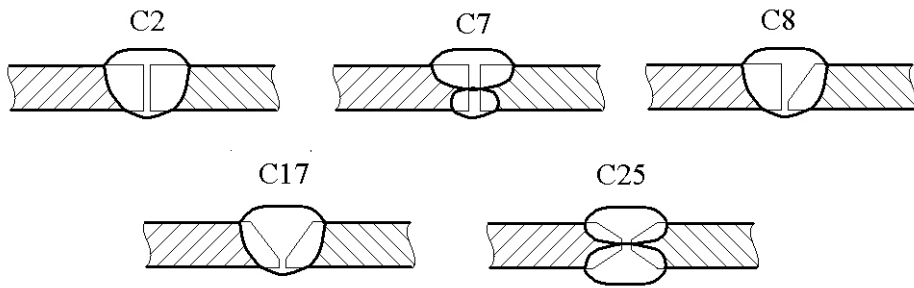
Некоторые типы стыковых сварных швов по ГОСТ 5264—80
